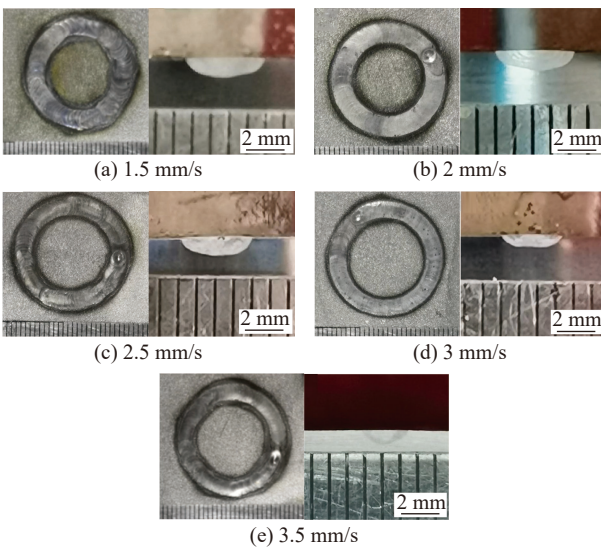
不同焊接速度下的焊缝成形及横截面
